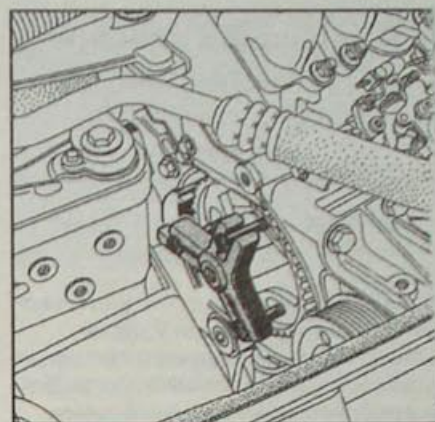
Установка приспособления Т.Аг. 1094 с тремя болтами М8х125
